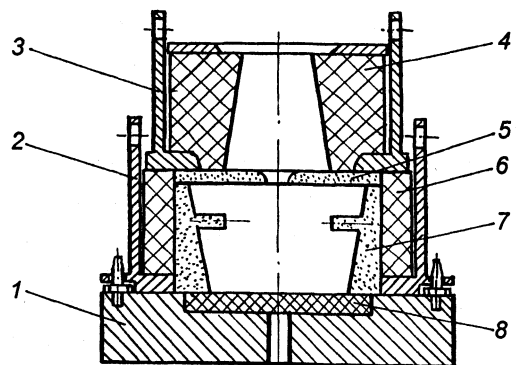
Опытная литейная форма: 1 – поддон; 2 – корпус формы; 3 – корпус прибыльной надставки; 4 – гнездовой кирпич; 5 – стержень-перемычка; 6 – шамотная кладка; 7 – формообразующий стержень вставки; 8 – графитовая вставка поддона
